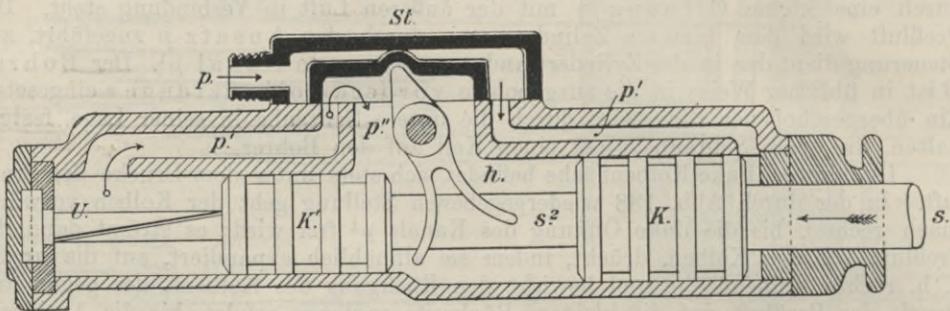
Prinzipskizze. Steuerung der Bohrmaschine Power Jumper.
